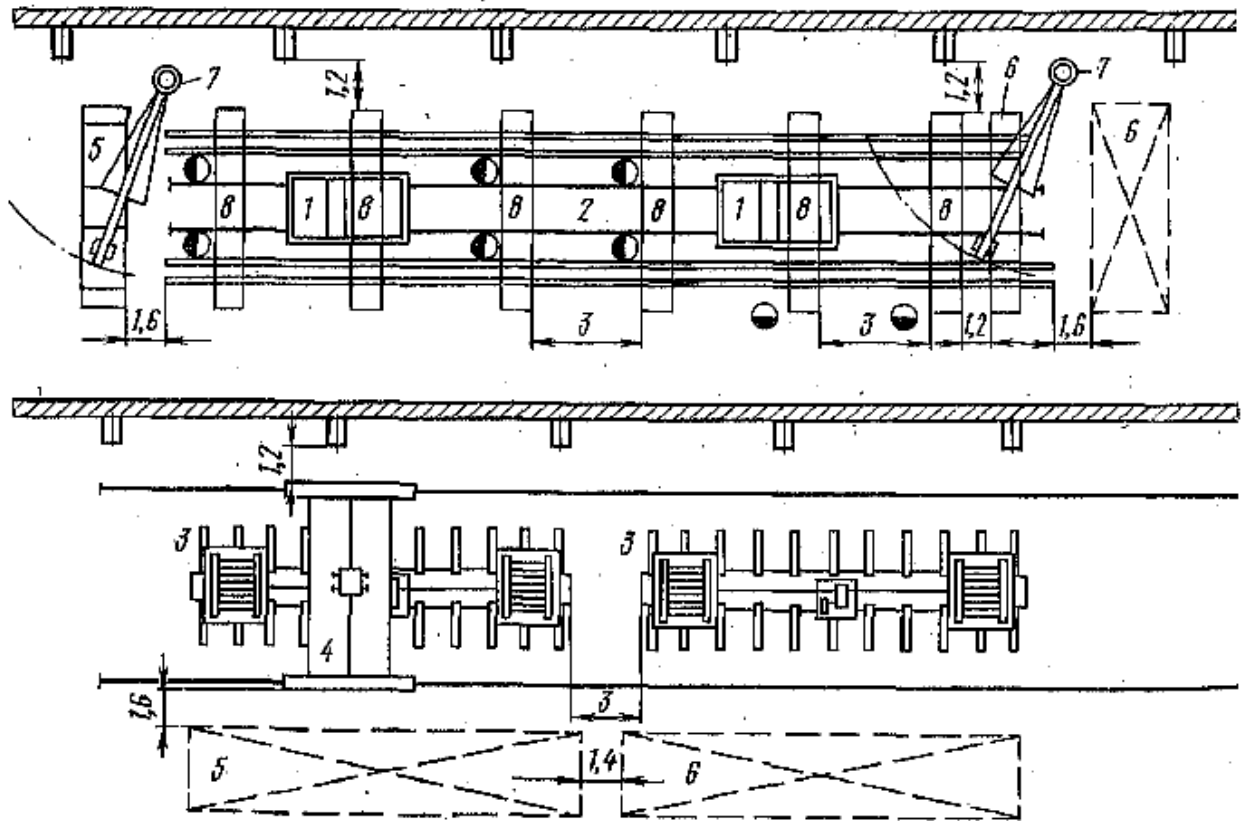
Схеми розташування установок для механізованого складання й автоматичного зварювання під флюсом балок та інших металевих конструкцій:
